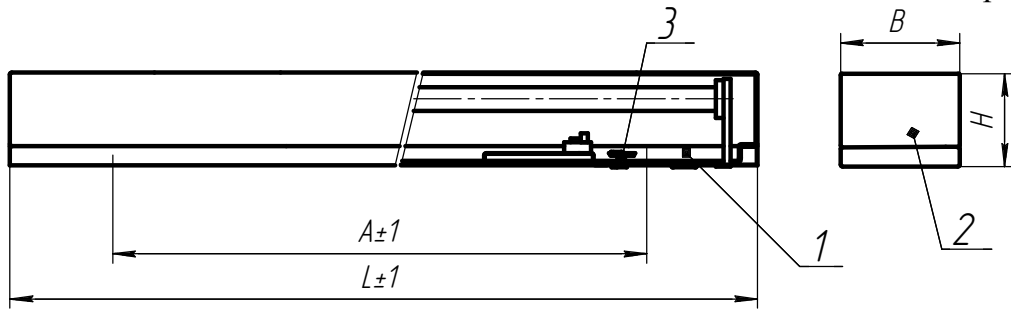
ЛПО46-18; 36; 2х18; 2х36 1. корпус в сборе; 2. рассеиватель; 3. зажим
